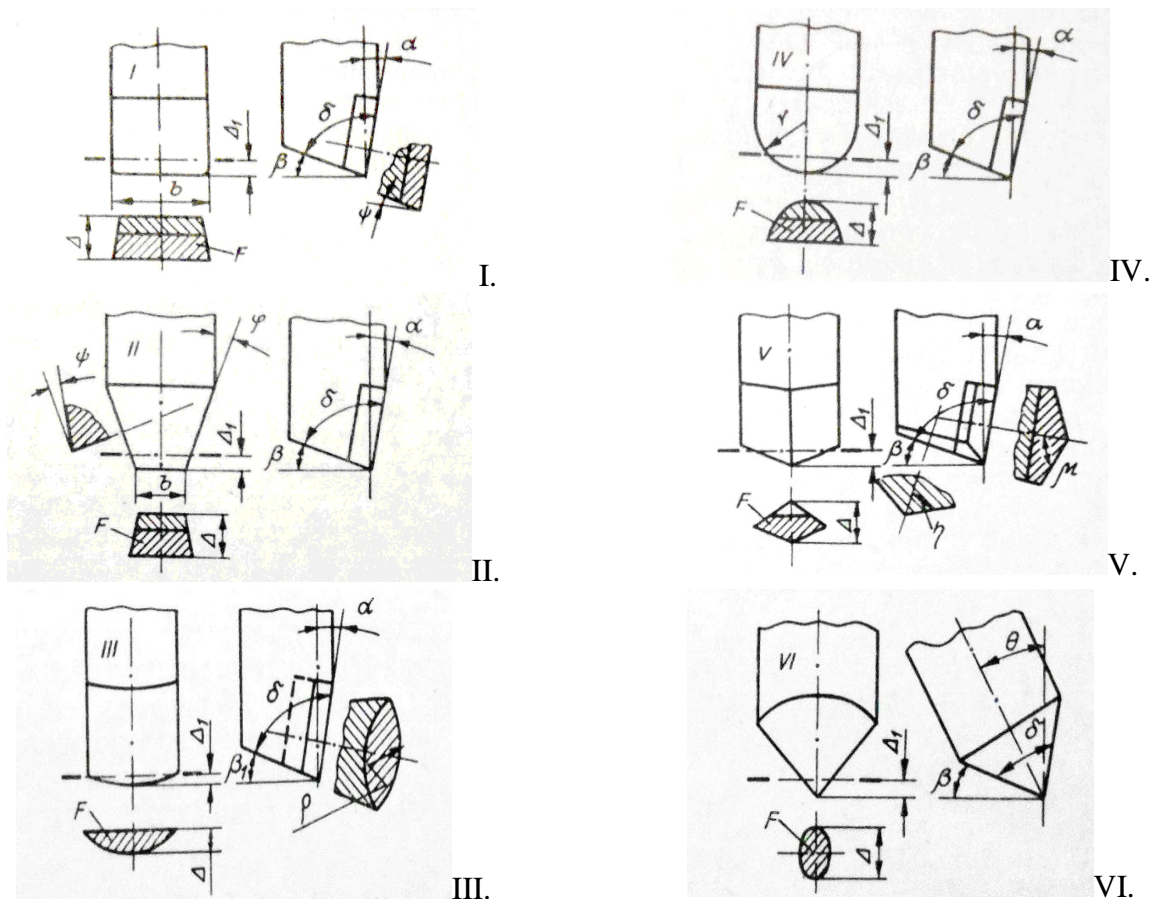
Схемы формы рабочей части основных типов резцов ( I – VI )
